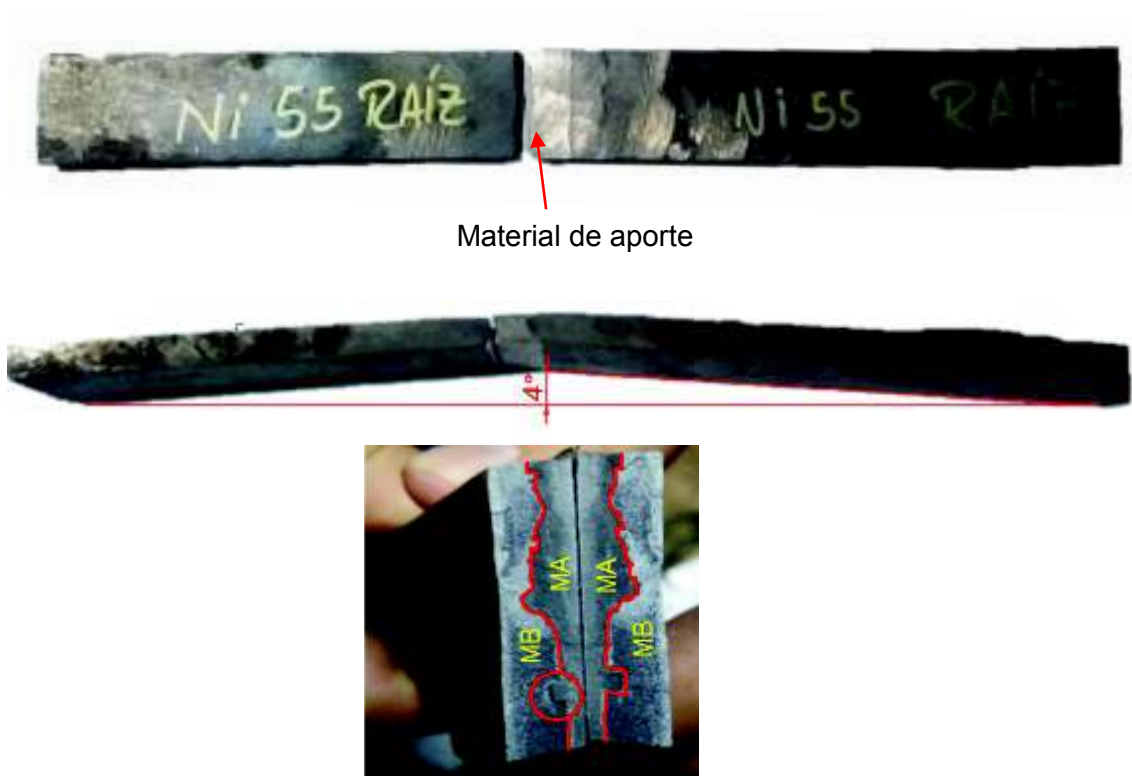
Doblado de raíz de la probeta soldada con M.A. AWS E NiFe - Cl.
